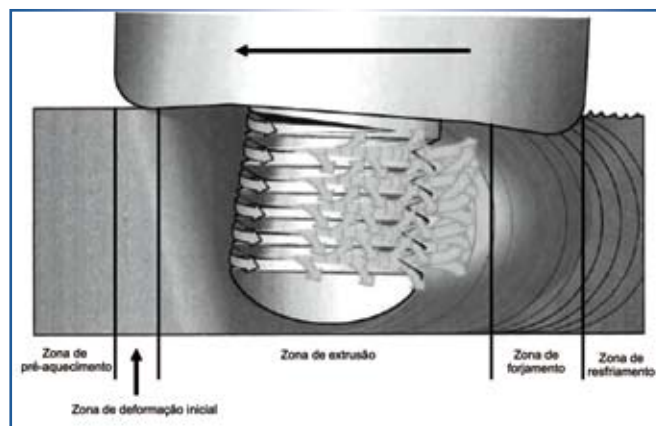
Representação do fluxo de material durante a soldagem por fricção linear (Paiva, 2009)
